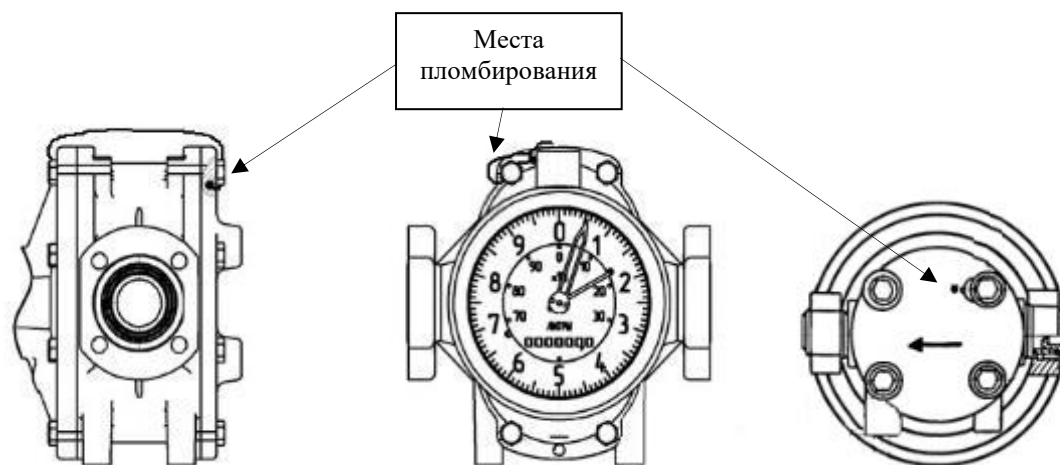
Схема пломбировки корпуса СК-ППО-М.
